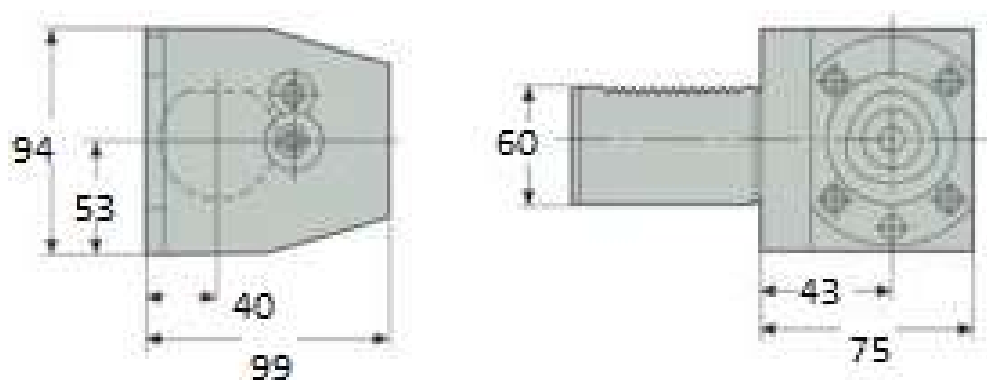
Резцедержатель C5-LC2060-43040M
